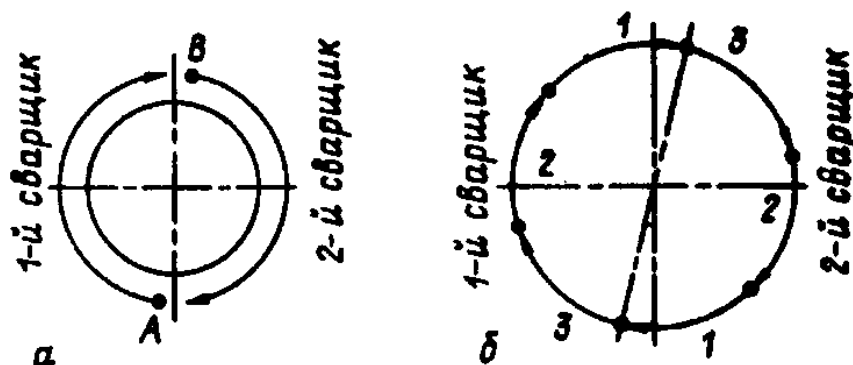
Порядок наложения первого слоя шва при сварке двумя сварщиками горизонтальных стыков труб:
